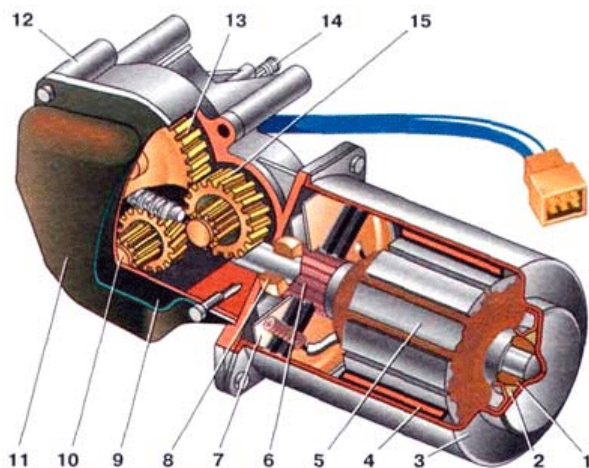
Моторредуктор стеклоочистителя 18.5215090-01 Kalina (автомобили семейства ВАЗ 1117-1119 «Калина» и их модификации, привод стеклоочистителя 181.5215100): 1 – задняя втулка вала якоря; 2 – войлочное кольцо; 3 – корпус электродвигателя; 4 – постоянный магнит; 5 – якорь; 6 – коллектор; 7 – траверса с щеткодержателями, дросселями и термобиметаллическими предохранителями; 8 – передняя втулка вала якоря; 9 – панель с помехоподавительными конденсаторами и контактами концевого выключателя; 10 – блок промежуточных шестерен; 11 – крышка; 12 – корпус редуктора; 13 – ведомая шестерня; 14 – выходной вал моторредуктора; 15 – блок промежуточных шестерен
